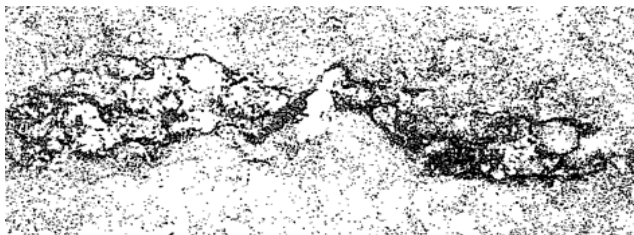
Неметалеві включення (місця скупчення шлаку) на поверхні заготовки
